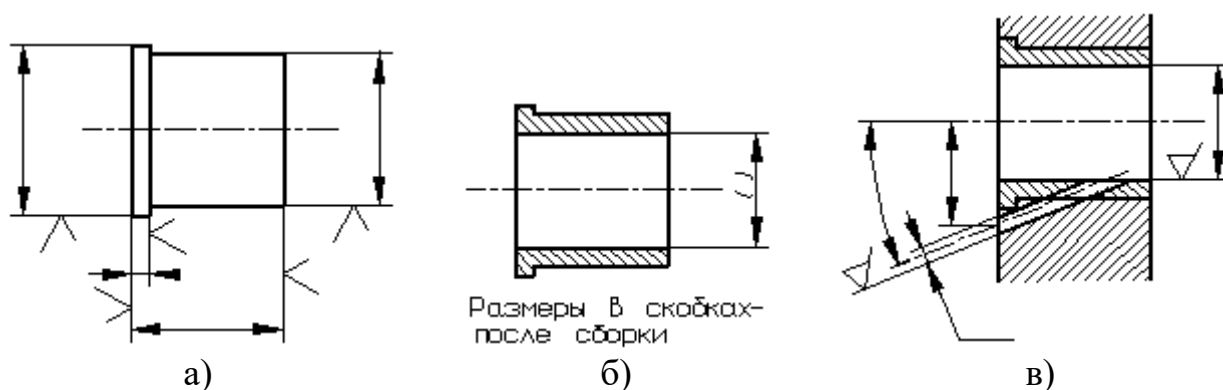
Указание размеров, предельных отклонений и шероховатости на рабочих чертежах: а) на чертеже изделия, которым оно должно соответствовать перед сборкой; б) на чертеже изделия с припуском на обработку в процессе сборки; в) на сборочном чертеже изделия
